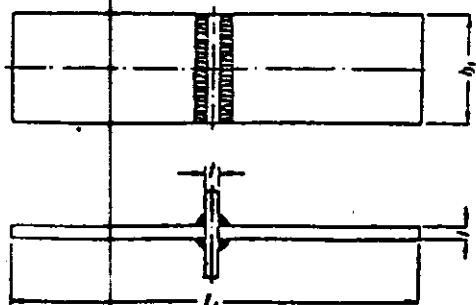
Zugprobe aus Schweißprobe 2
